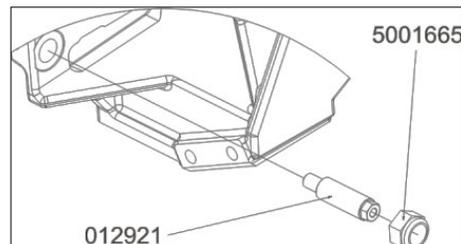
VUE ARRIÈRE – BORNE DE MASSE
